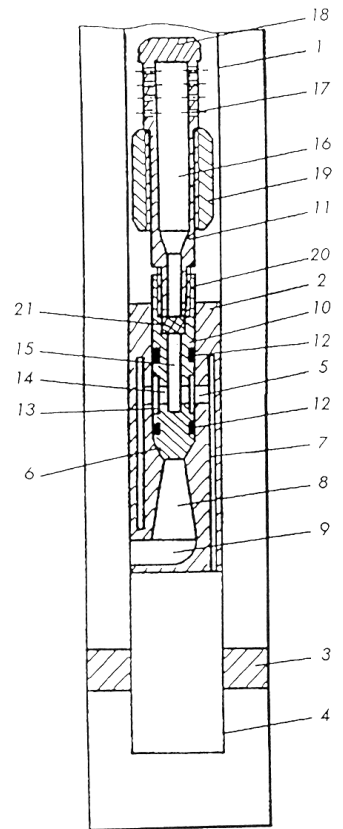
3. Схема погружного оборудования струйной насосной установки при опрессовке пакера сверху:
